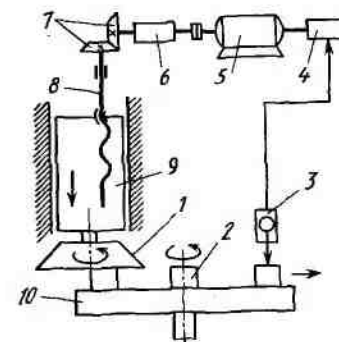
Схема подналадочной системы плоскошлифовального станка
